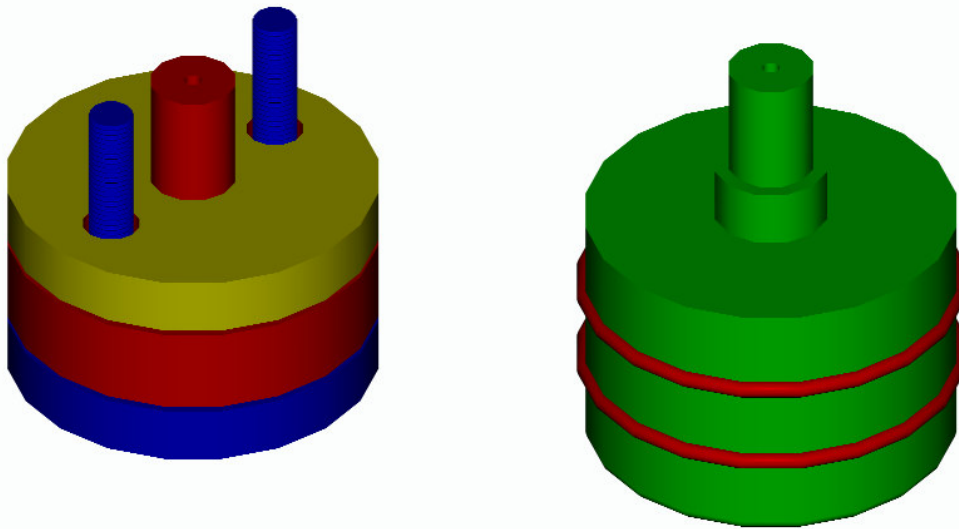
(a) Desenho da Tampa com o uso de um elastômero (b) Desenho da tampa com o uso de anéis de borracha (o-rings).
